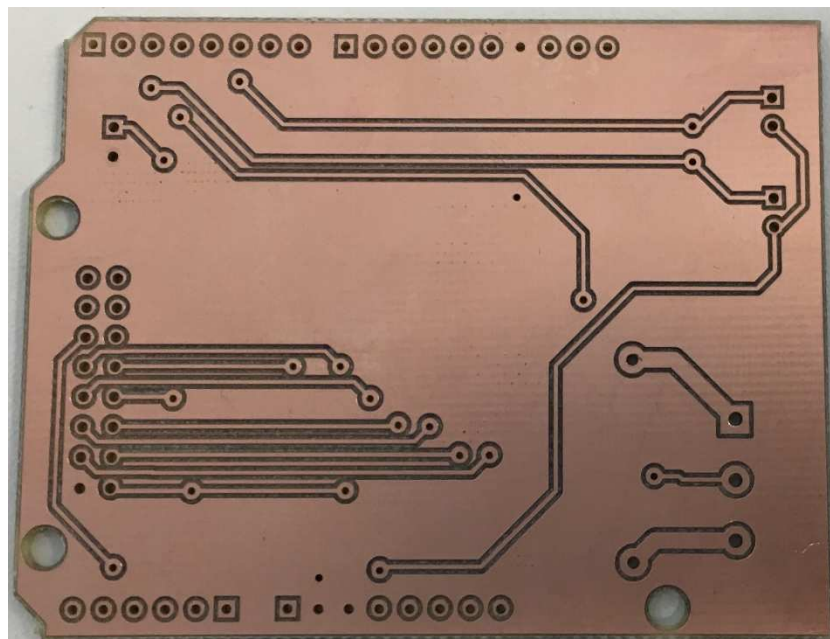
Foto de la cara inferior (*BottomLayer*) de la PCB de control.
